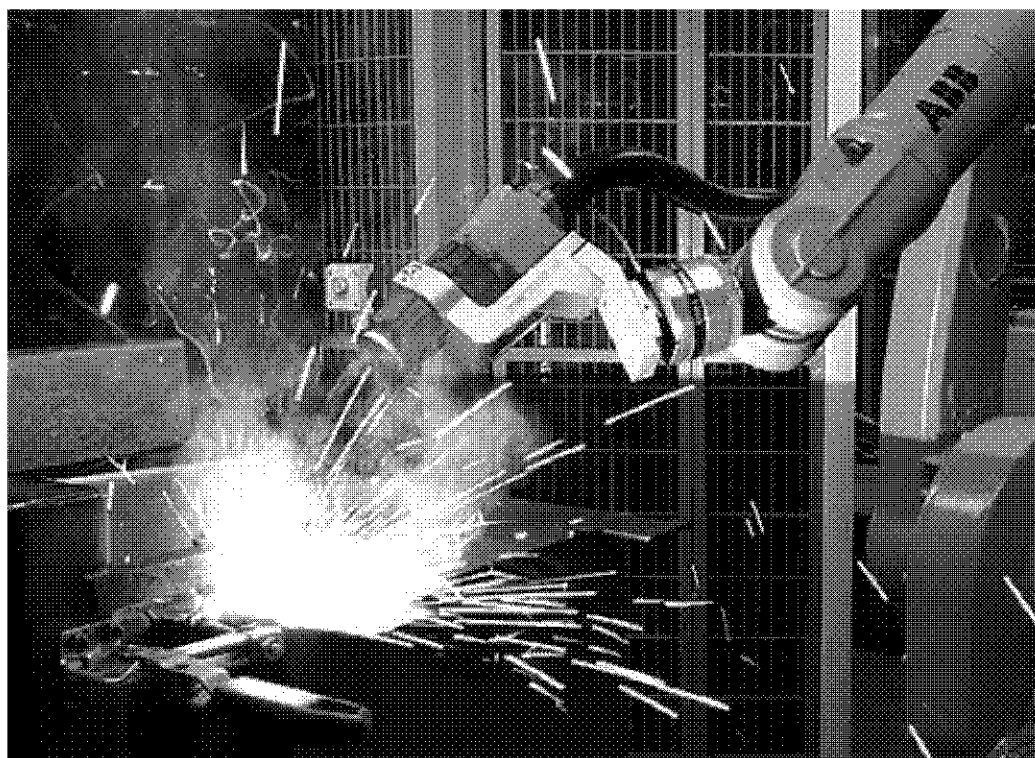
Промышленный робот для электродуговой сварки
